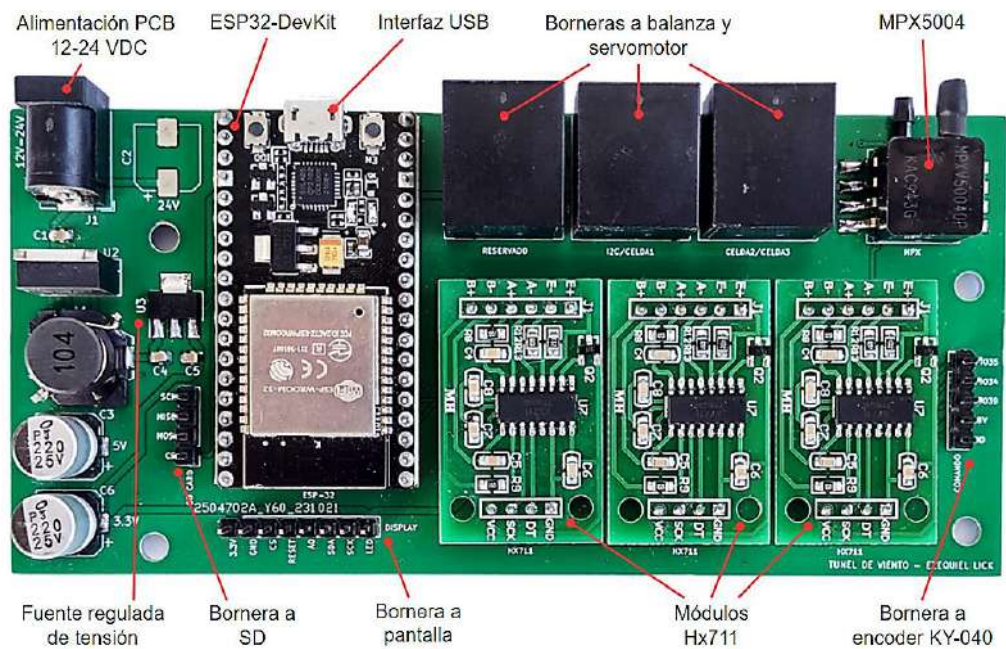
Cara frontal de la placa PCB con componentes soldados.
